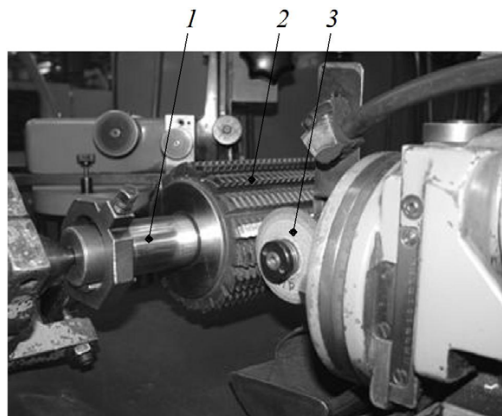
Затылование зубьев червячной фрезы: 1 – оправка; 2 – заготовка фрезы; 3 – шлифовальный круг
